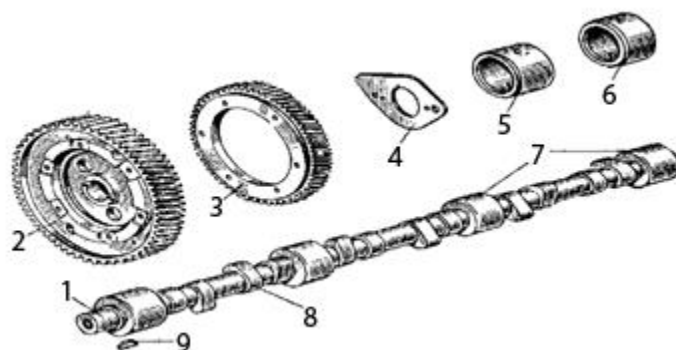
Распределительный вал V-образного дизеля, детали его привода и установки: 1 – распределительный вал; 2 – шестерня привода распределительного вала; 3 – шестерня привода топливного насоса высокого давления; 4 – упорный фланец; 5 – передняя втулка распределительного вала; 6 – втулки; 7 – шейки распределительного вала; 8 – кулачки; 9 - шпонка
